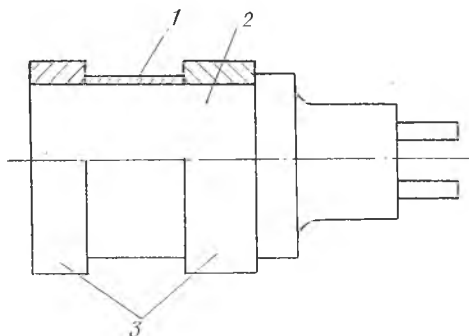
Экспериментальная раздача трубчатого образца при магнитно-импульсном деформировании: 1 — трубчатый образец; 2 — индуктор; 3 — металлические кольца
